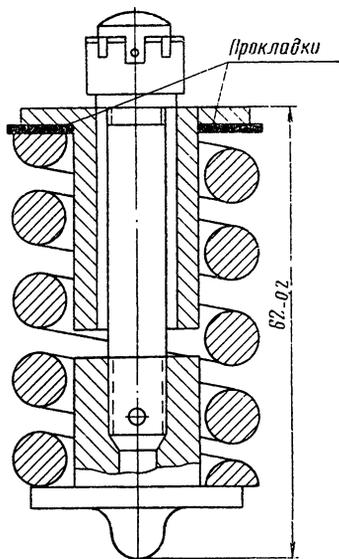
Сборка и установка уравновешивающей пружины тормозного крана
